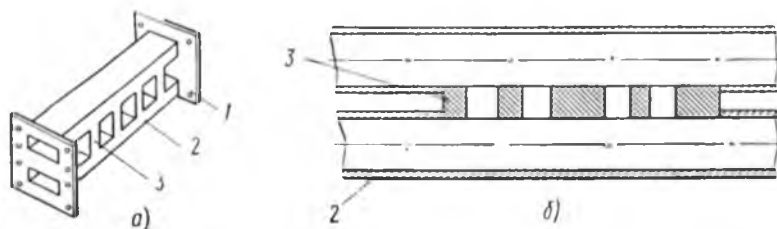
Волноводный направленный ответвитель со связью через шлейфы (а), конструкция зоны связи при малой длине шлейфов (б):
